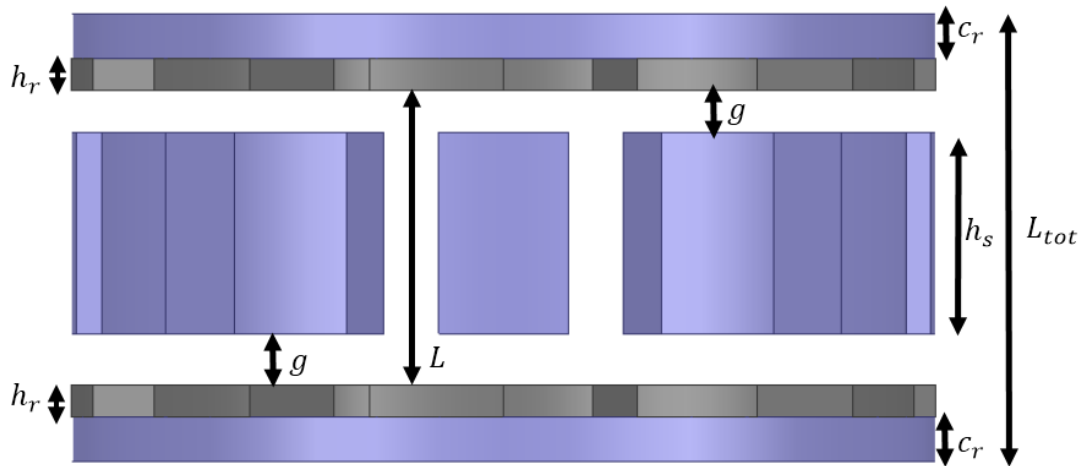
Vista frontal do rotor e estator com as variáveis dimensionais.
